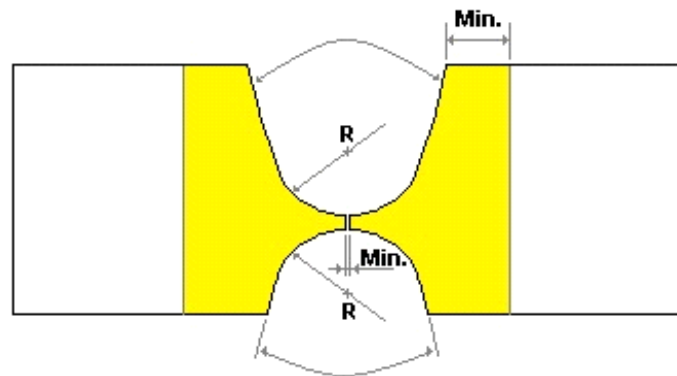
Immagine tipica di un giunto con tecnica di "imburraggio"
